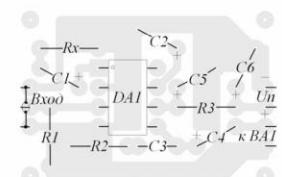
Эскиз монтажной платы усилителя. Вид со стороны расположения деталей
